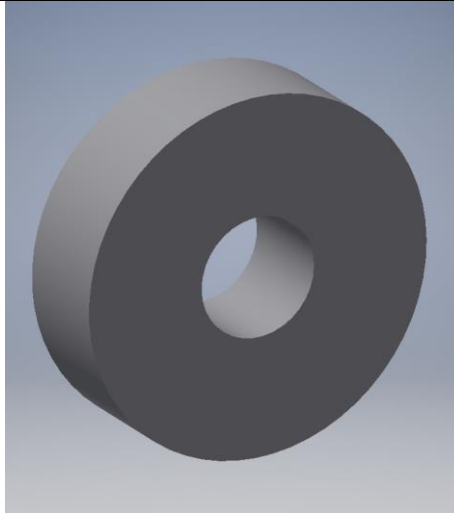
Placă de bază matriță tubulară (desen execuție planșa 2/16)
